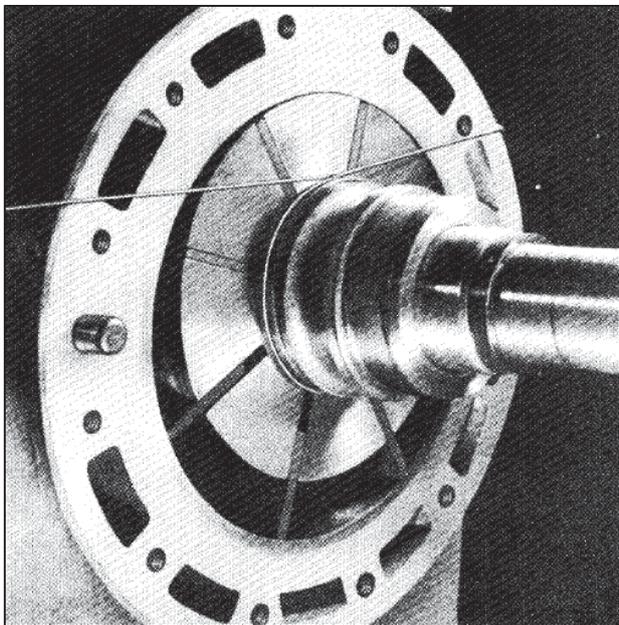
Перед установкой головки цилиндра обожмите уплотнительное кольцо.
